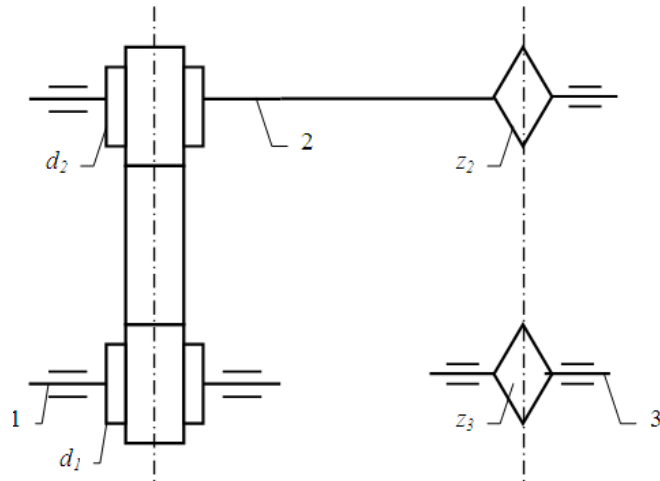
Кинематическая схема привода с ременно-цепным передаточным механизмом
